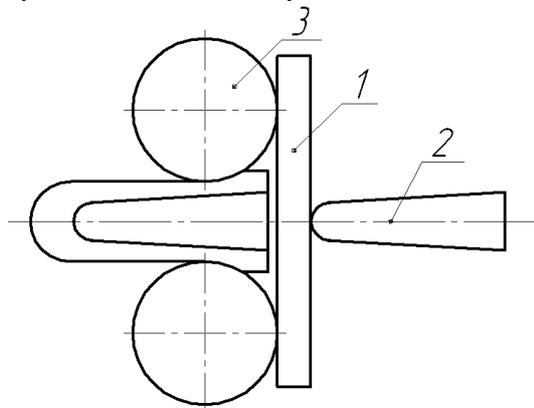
Схема прокатки параболических заготовок малолистовых рессор на профильной оправке
